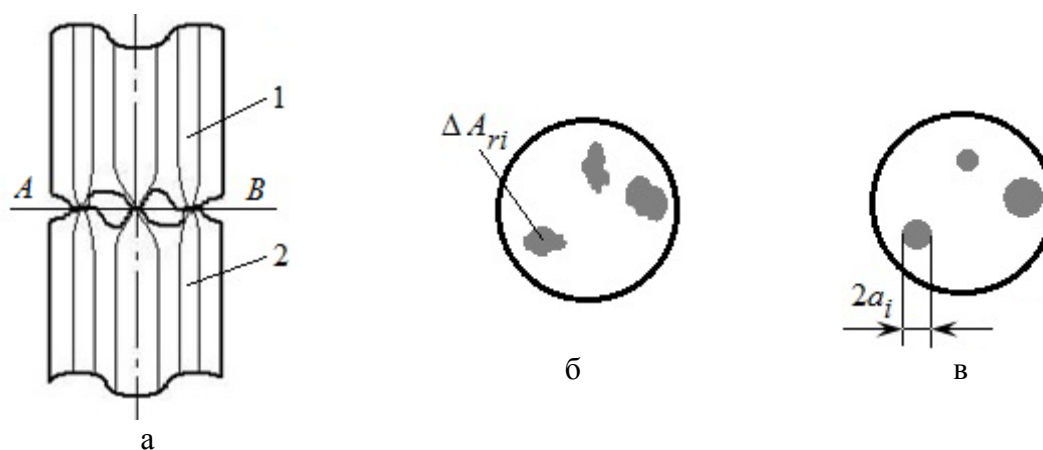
Контакт двух деталей с шероховатыми поверхностями:
